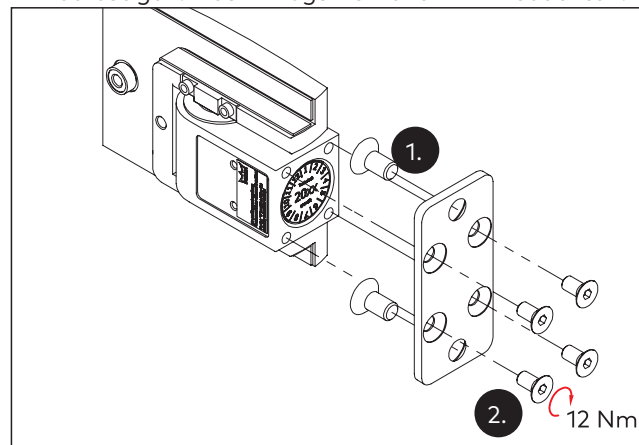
Befestigung der Montageplatten am Pendeltürband
